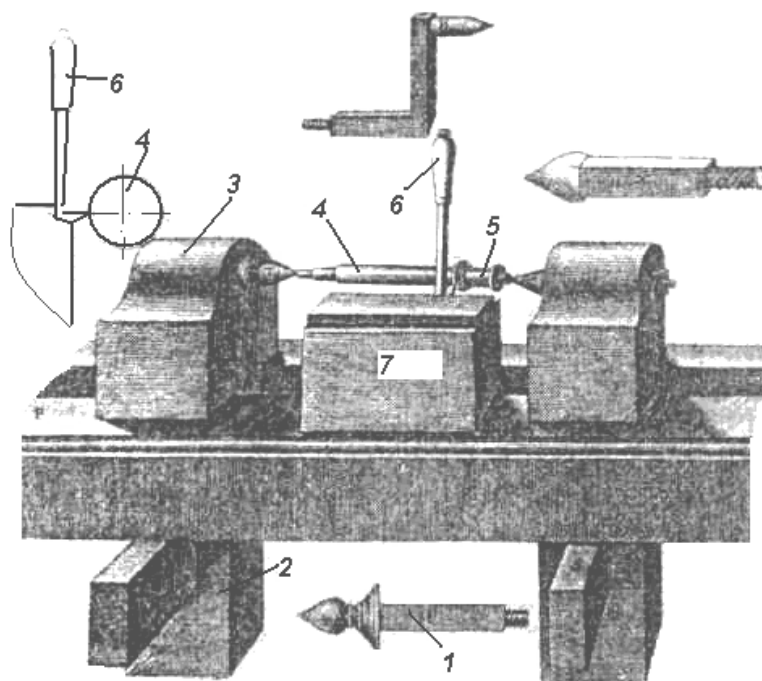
Токарный металлорежущий станок (Плюмье, 1701 г.)
